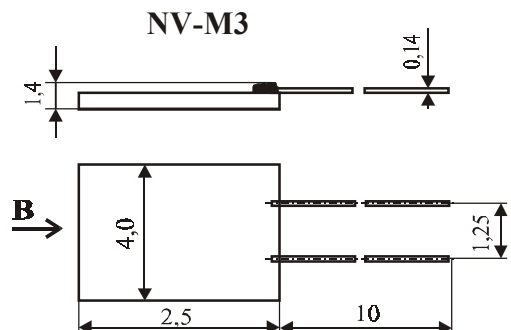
Внешний вид и габаритные размеры магниторезисторов NV-M3
